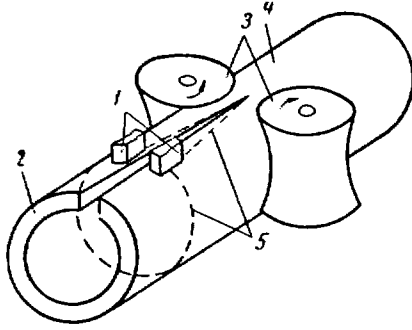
Схема высокочастотной сварки с контактным подводом тока:
